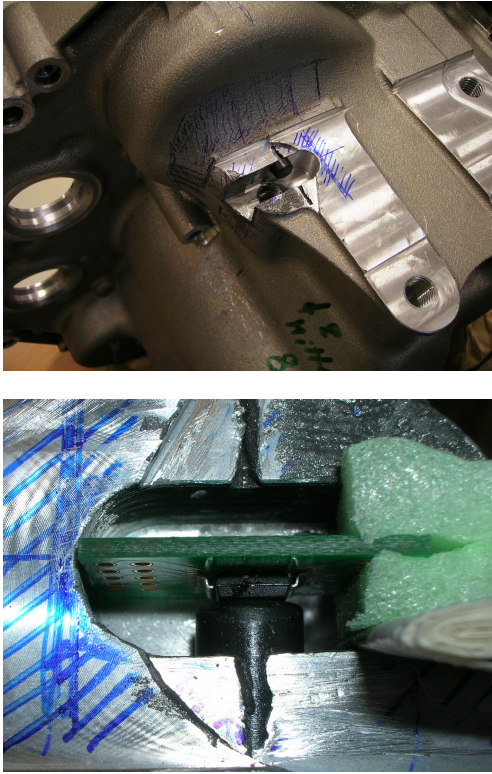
Einpassen des Sensors in die Fräsung
